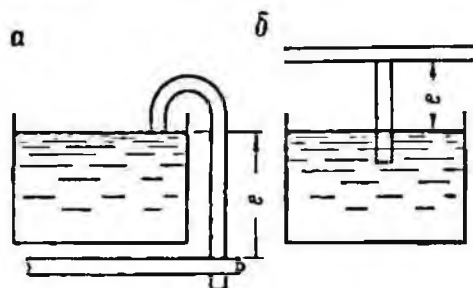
Системы смазки с использованием сил капиллярности для смазки:
